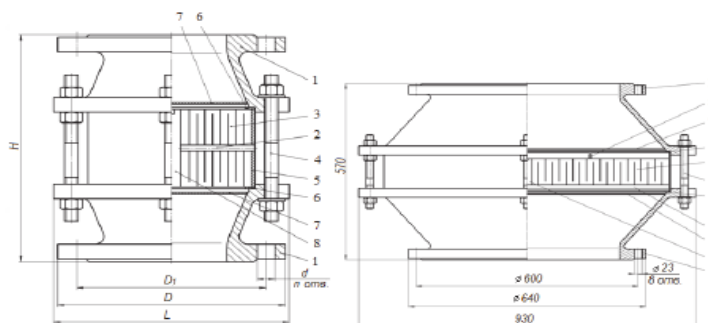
Запобіжники вогневі: а - ОП-100 ... ОП-350; б - ОП-500 1 - корпус; 2 - кільце; 3 - касета; 4 - шпильки; 5 - обмежувачі; 6 - прокладка; 7 - заглушка; 8 – вогнеграничний елемент
